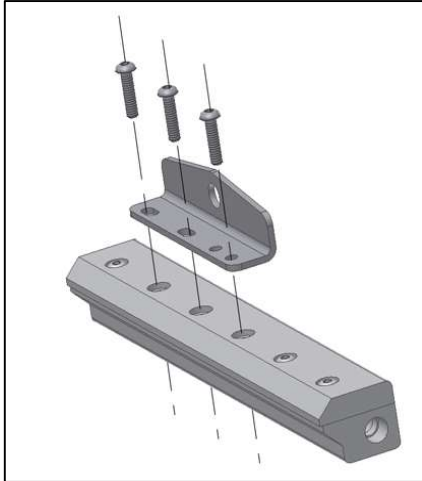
Super Air Knife 12" (305 mm) aus Aluminium
